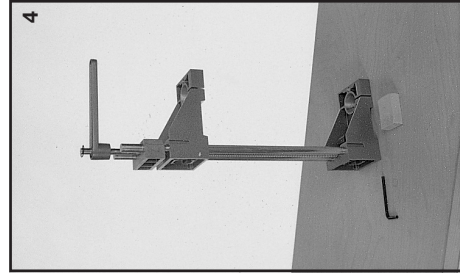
Schrauben (b5) an unterer Systembacke (b) lösen; gewünschte Neigung einstellen. Schrauben (b5) wieder fixieren. Tiefenanschlag mit Klemmhalter (h1).
